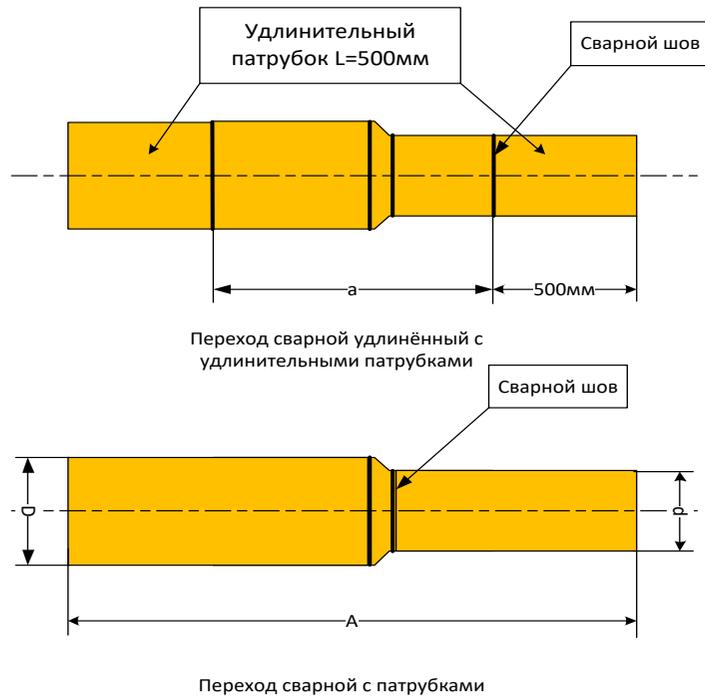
Варианты исполнения соединений полиэтиленовых труб и фитингов (переход сварной удлиненный с удлинительными патрубками)
